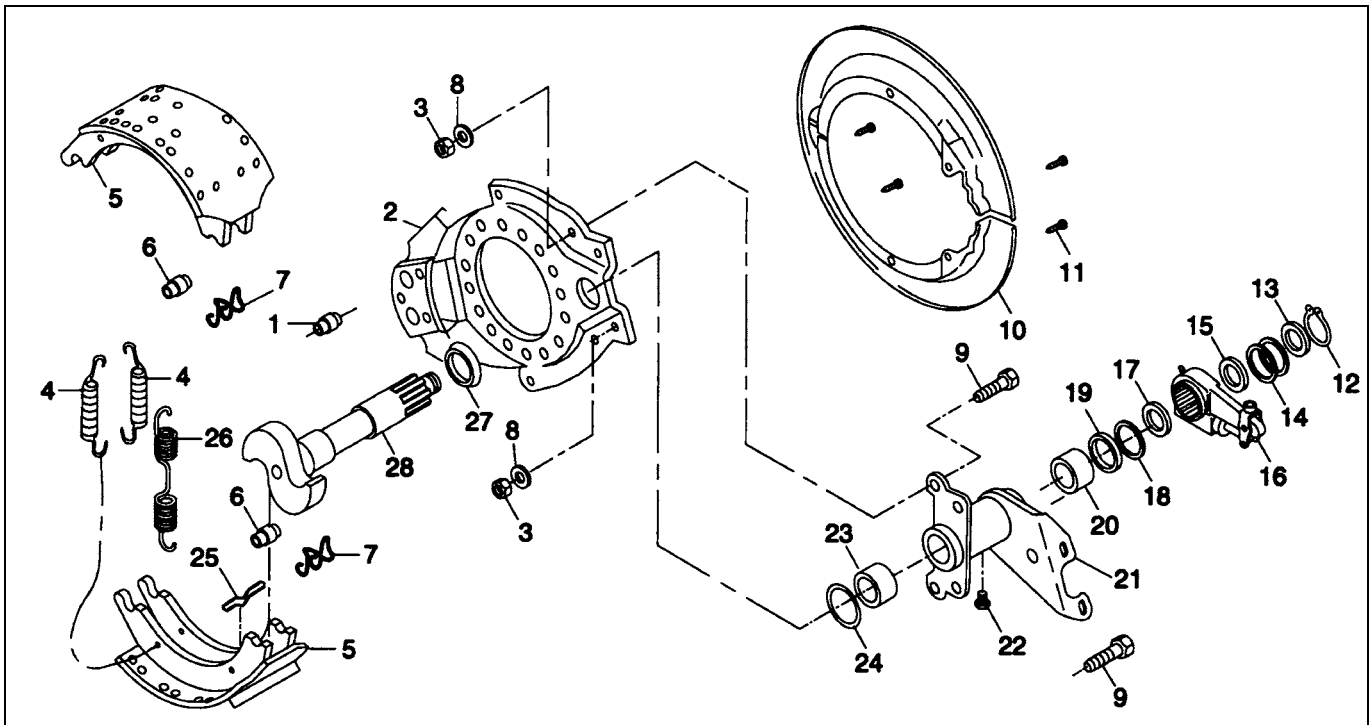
Тормоз Q Plus серии MX500 со штампованным опорным диском. 1 - анкерный палец, 2 - опорный диск, 3 - гайка (4 шт.), 4 - фиксирующая пружина, 5 - тормозная колодка в сборе, 6 - ролик кулачка, 7 - клипса ролика, 8 - закаленная шайба (4 шт.), 9 - болт (4 шт.), 10 - пыльник, 11 - болт пыльника, 12 - стопорное кольцо кулачкового вала, 13 - шайба/прокладка, 14 - тонкая прокладка, 15 - оранжевый сальник, 16 - автоматический компенсатор износа, 17 - сальник, 18 - толстая прокладка, 19 - сальник, 20 - втулка кулачкового вала (1-1/2 дюйма), 21 - кронштейн кулачкового вала и тормозной камеры, 22 - пробка, 23 - втулка кулачкового вала (1-5/8 дюйма), 24 - оранжевый сальник, 25 - палец возвратной пружины, 26 - возвратная пружина, 27 - упорная шайба с фаской, 28 - кулачковый вал.
